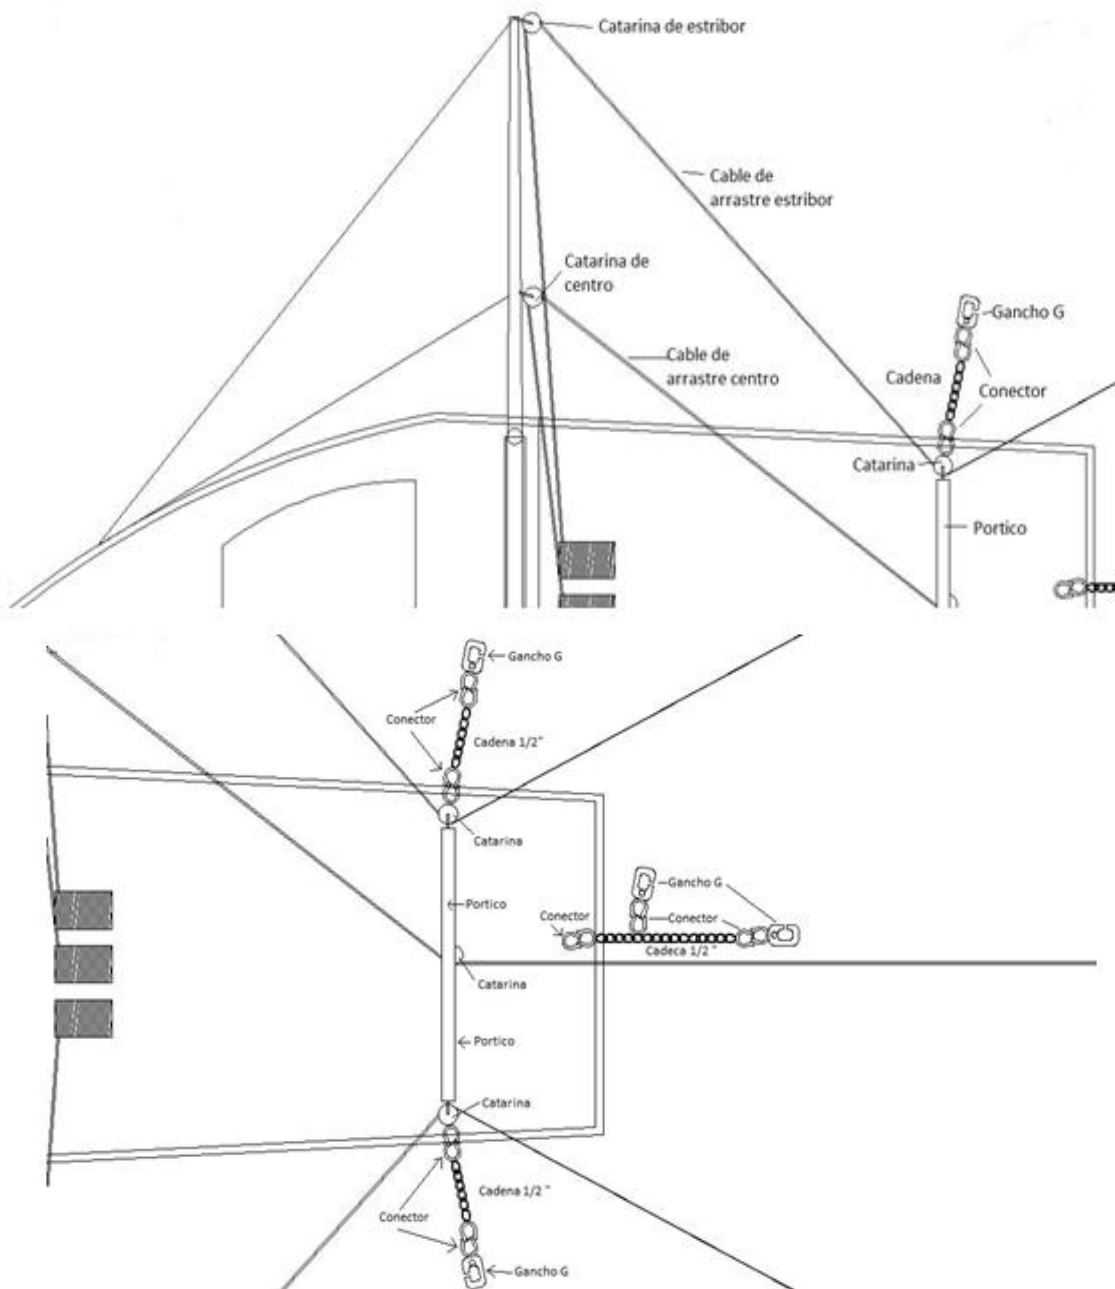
Detalle B y C, elementos del tangón de estribor y popa.
